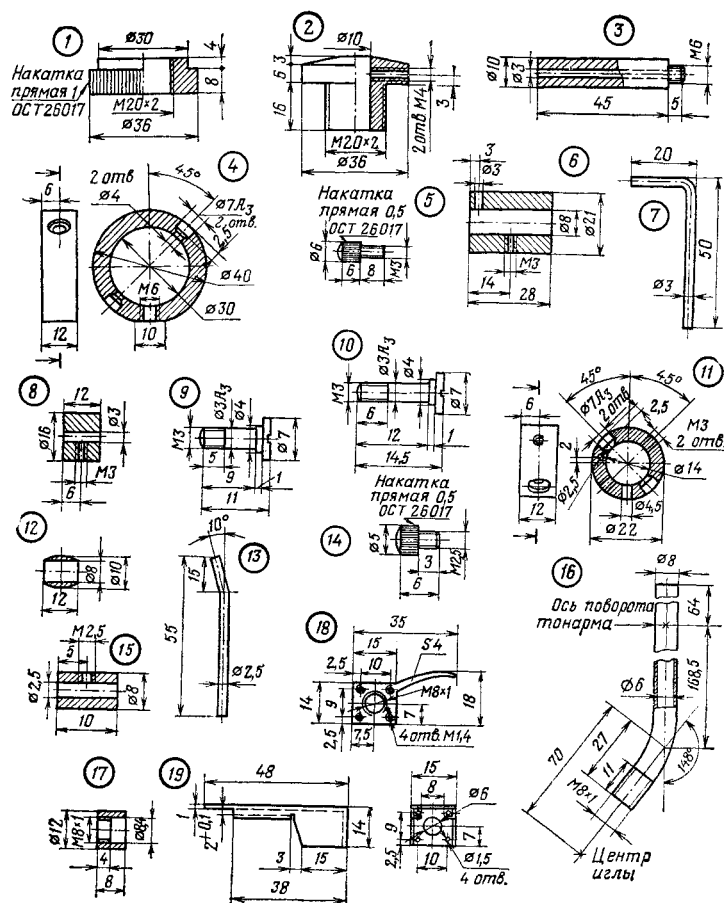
Детали тонарма: 1 — гайка; 2 — основание; 3 — стойка; 4 — кольцо большое; 5 — винт, 2 шт.; 6 — противовес большой; 7 — стержень, закрепить в дет. 6 эпоксидным клеем; 8 — противовес малый; 9 — винт специальный, 2 шт.; 10 — винт специальный, 2 шт.; 11 — кольцо малое; 12 — кольцо, приклеить к дет. 16 эпоксидным клеем; 13 — стержень компенсатора скатывающей силы, закрепить в дет. 11 эпоксидным клеем; 14 — винт; 15 — грузик; 16 — трубка тонарма, покрасить черной нитроэмалью; 17 — гайка; 18 — планка; 19 — держатель головки, закрепить на дет. 18 четырьмя винтами М1, 4×4. Материал деталей 1—4, 11, 12, 16—18 — Д16-Т; 5, 6, 8 — 10 — ЛС59-1; 7 и 13 — Ст. 4Х13; 19 — Л62-М. Детали из латуни хромировать.
